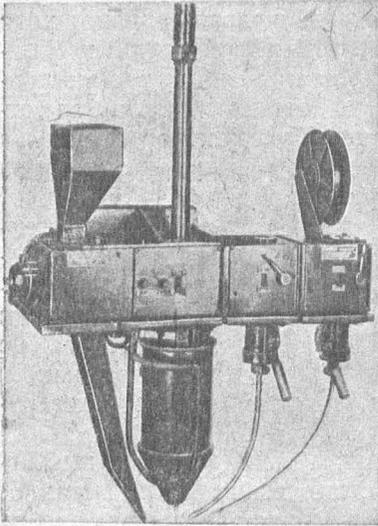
Автоматическая головка Сименс-Шукерт для сварки в защитной атмосфере
